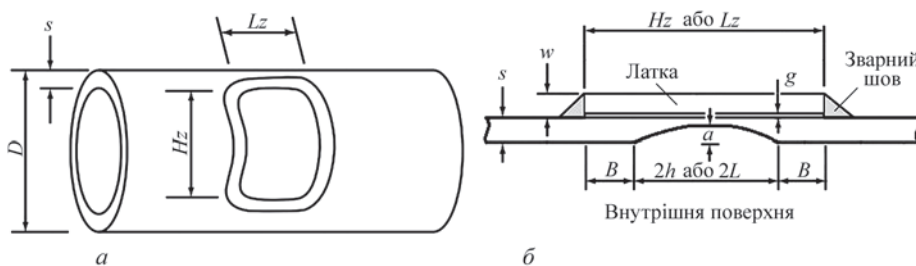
Схема підсилення дефектної ділянки трубопроводу зварною накладною латкою: а – загальний вид трубопроводу із встановленою латкою; б – переріз у зоні накладної латки
